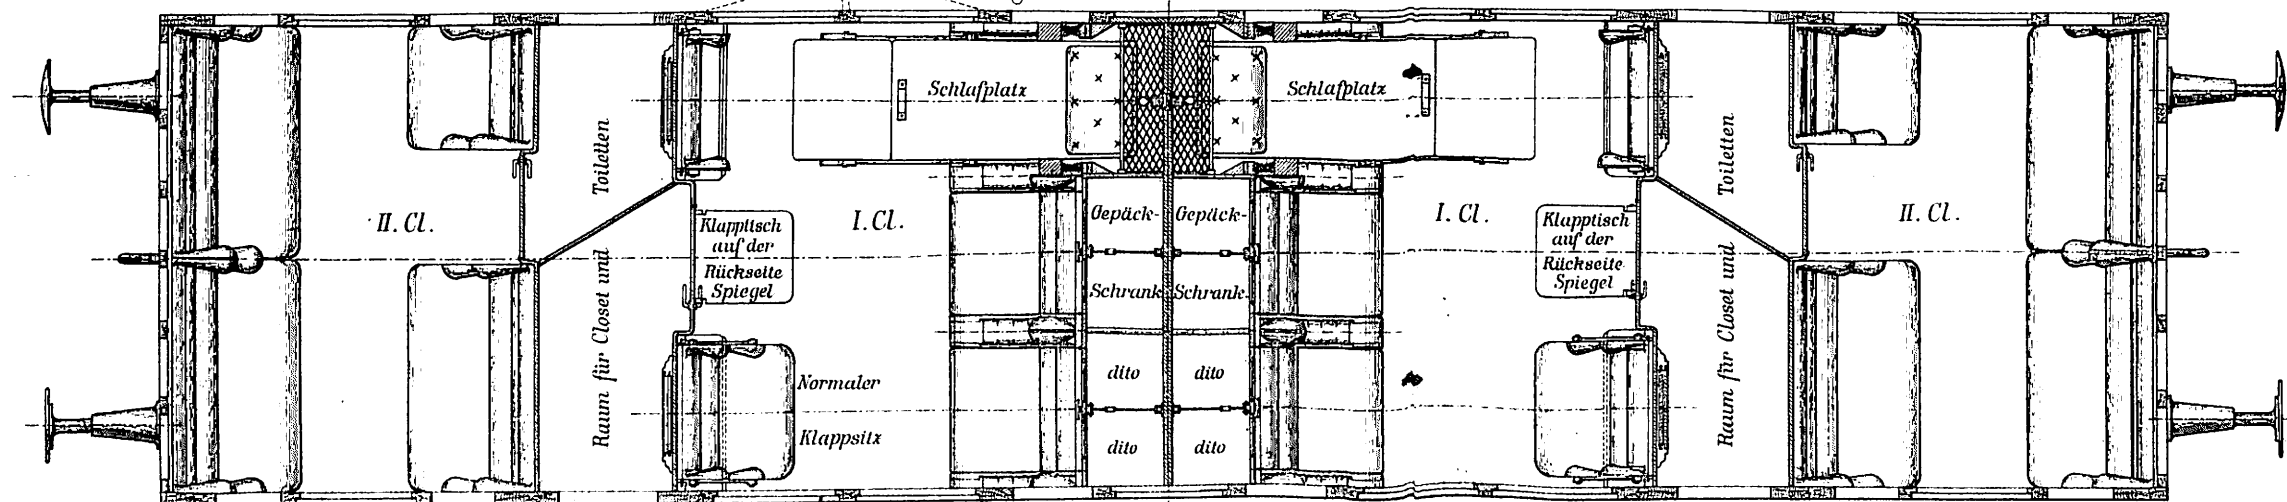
Grundriss. Maassstab 1:40.
